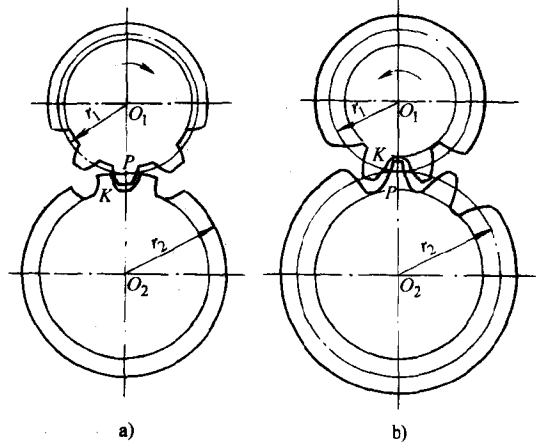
单圆弧齿轮传动和双圆弧齿轮传动
